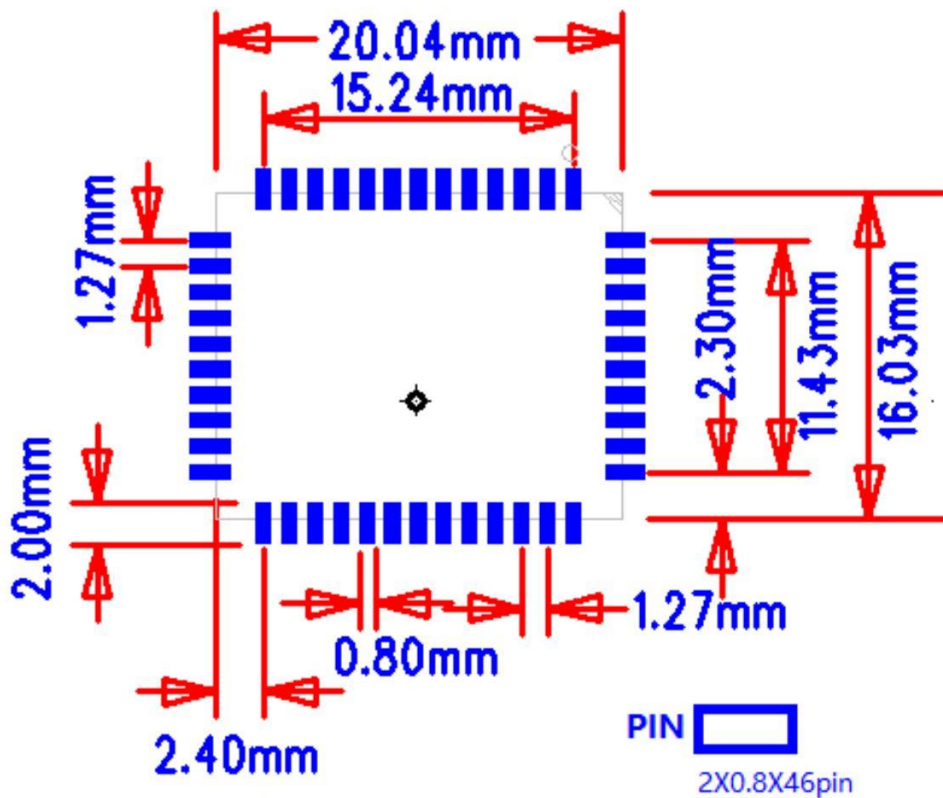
推荐 PCB 封装尺寸图 (单位: 毫米) (TOP 视图)
